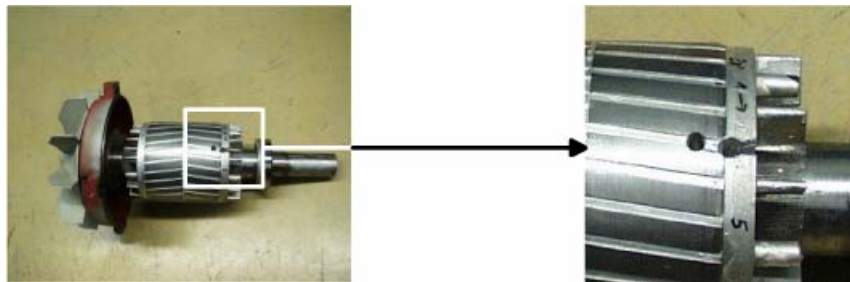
Rotor der defekten Asynchronmaschine mit aufgebohrtem Stab und Kurzschlussring
